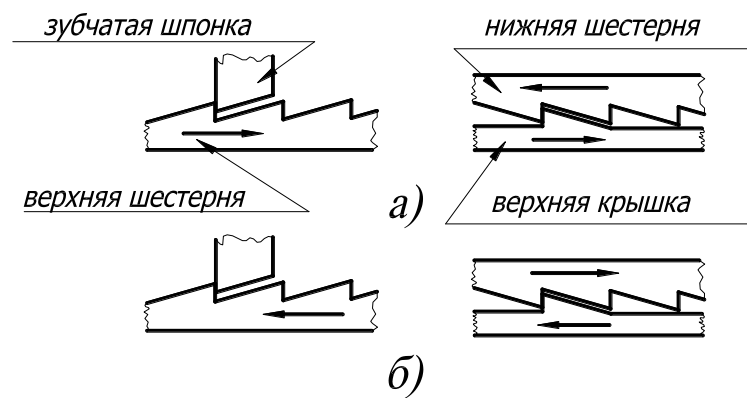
Схема зачеплення зубчатої шпонки і верхньої шестерні, а також верхньої кришки і нижньої шестерні при повороті поворотного кулака: а) вправо; б) вліво.
